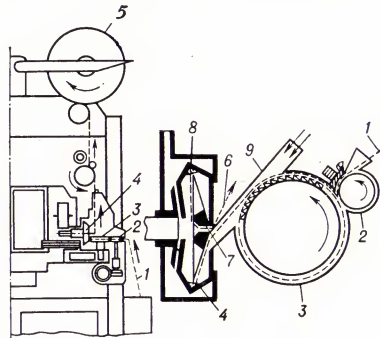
Схема пневмомеханической прядильной машины: 1 — лента; 2 — питающий цилиндр; 3 — дискретизирующий, или расчёсывающий, валик; 4 — прядильная камера; 5 — бобина; 6 — пряжа; 7 — направляющая трубка; 8 — желоб; 9 — канал.
